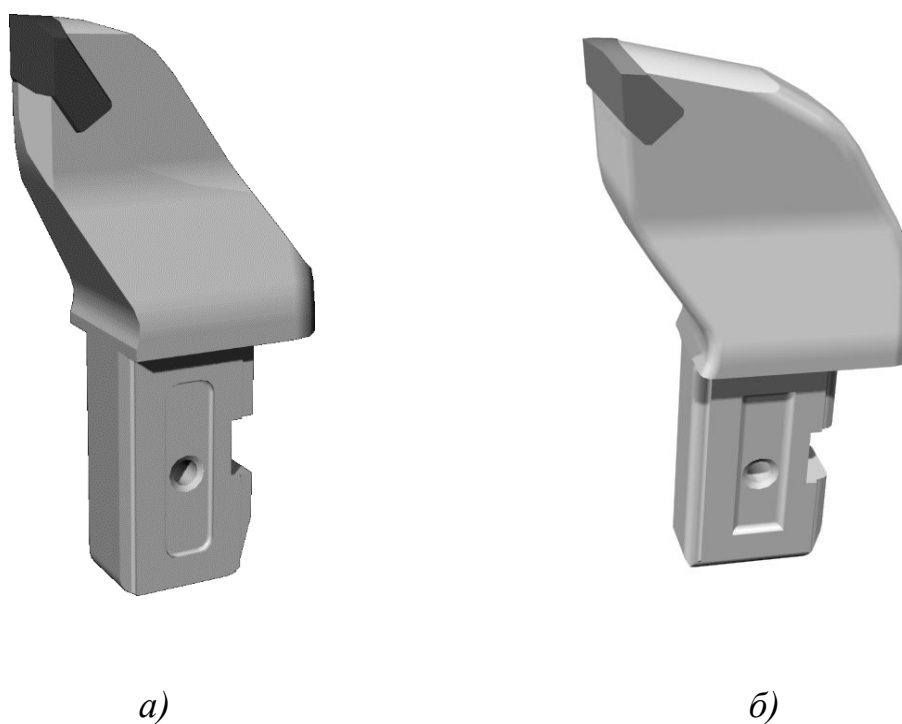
Вид резца типа ЗРБ2-80 с овально-конической а)
